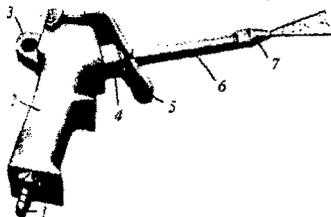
Пистолет для обдувки деталей сжатым воздухом мод. С-417
